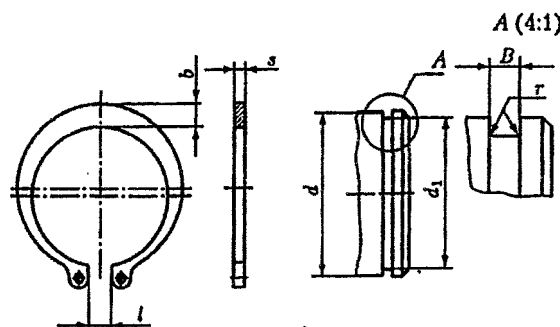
Кольца пружинные упорные эксцентрические наружные и канавки для них
